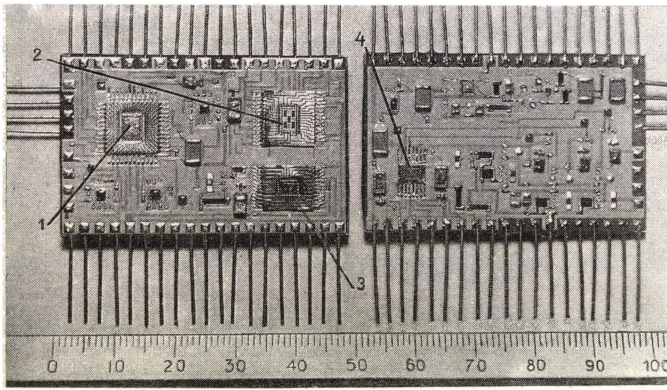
Внешний вид гибридной микросборки без корпуса сверху и снизу:
